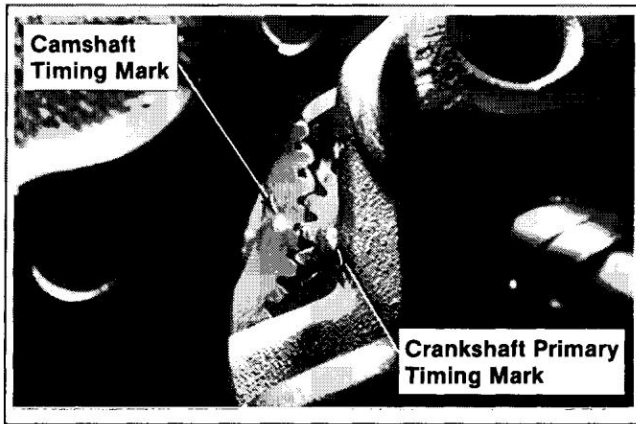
Alignement du pignon d'arbre à cames et Engrenage de vilebrequin.
